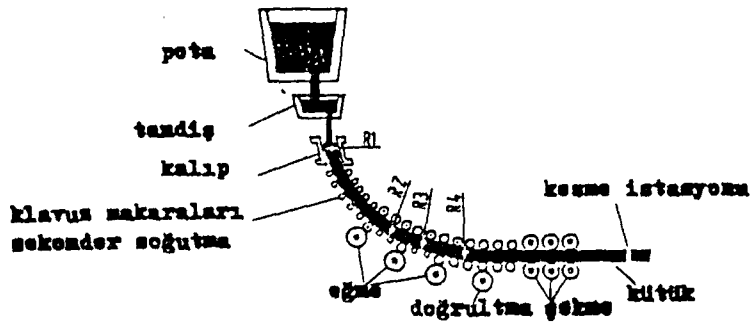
Düz kalıp ve çember kavisli döküm yollu düşey sürekli döküm tarzı
